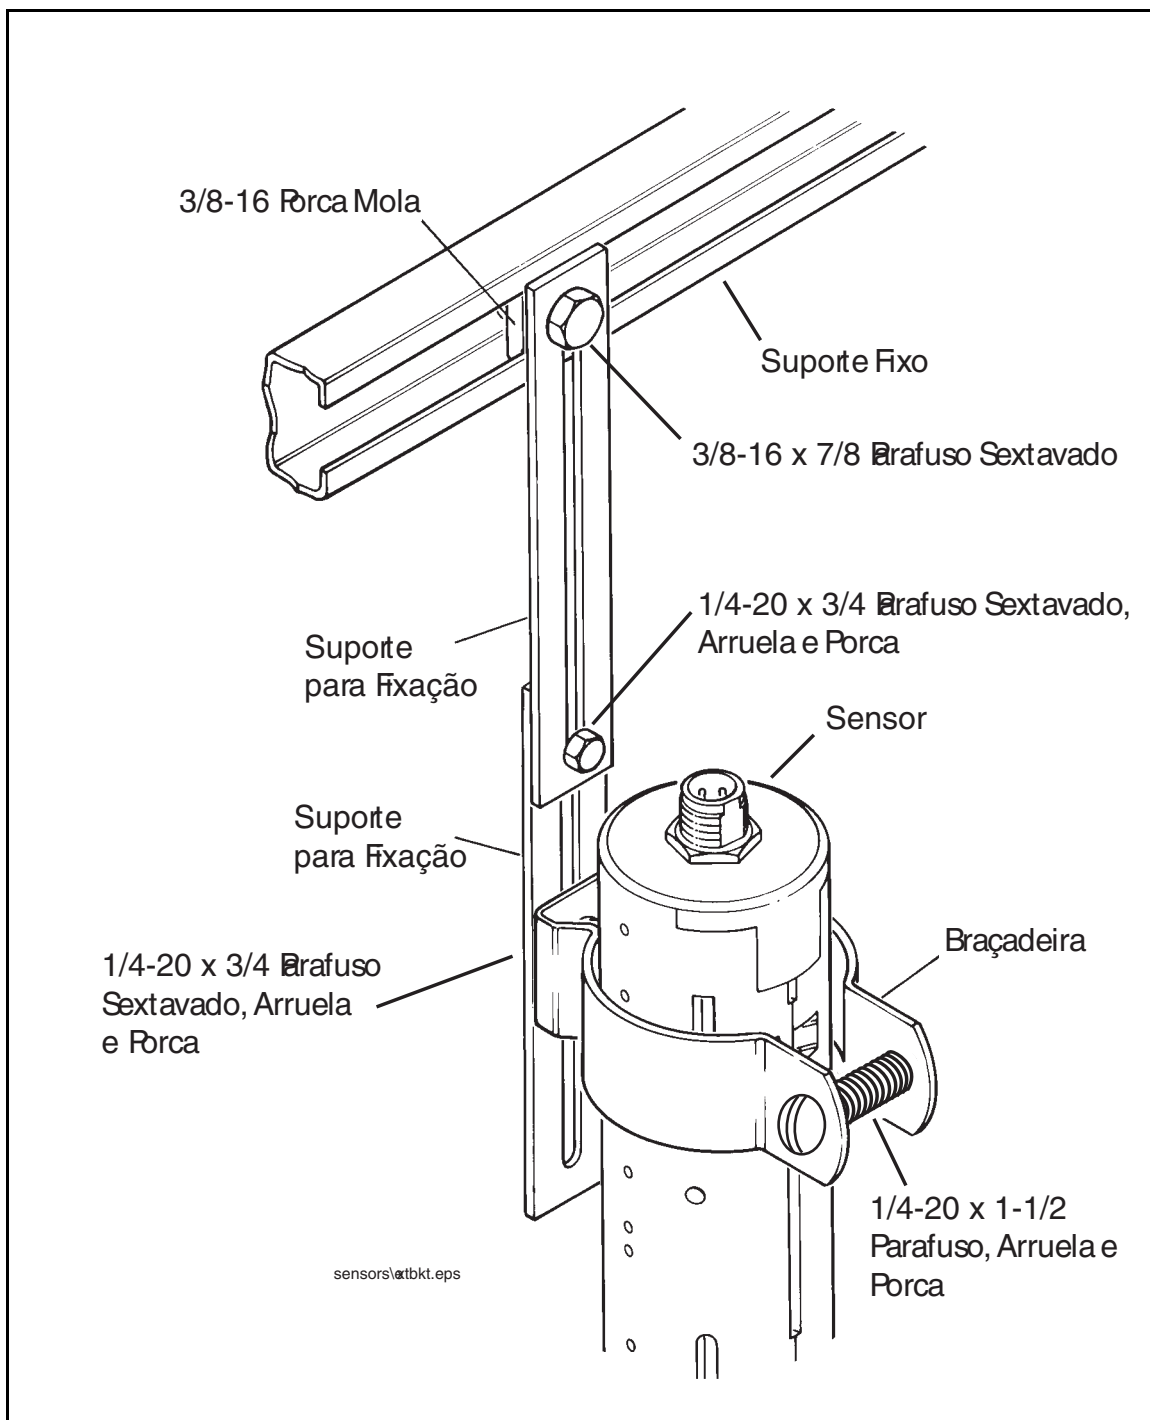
Montagem do Kit com auxílio de dois Suportes
